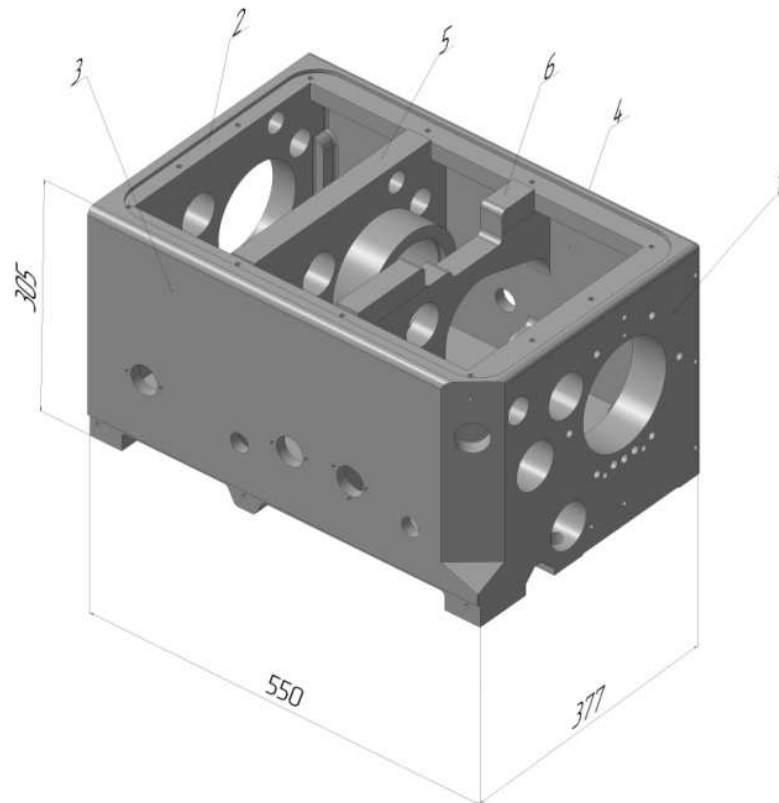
3-Dмодель корпуса передней бабки станка 16Б16П
